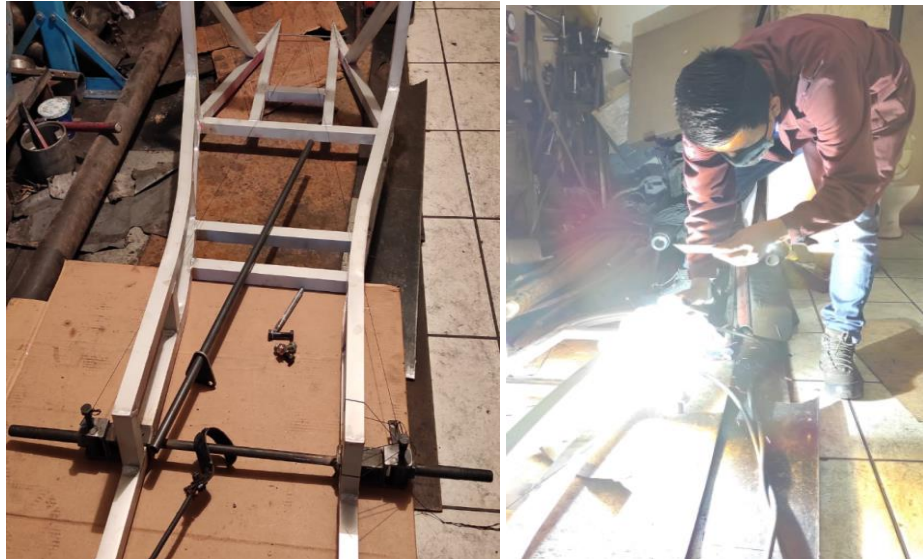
Señalización, punteado, soldado y pulido del perno y la mangueta
